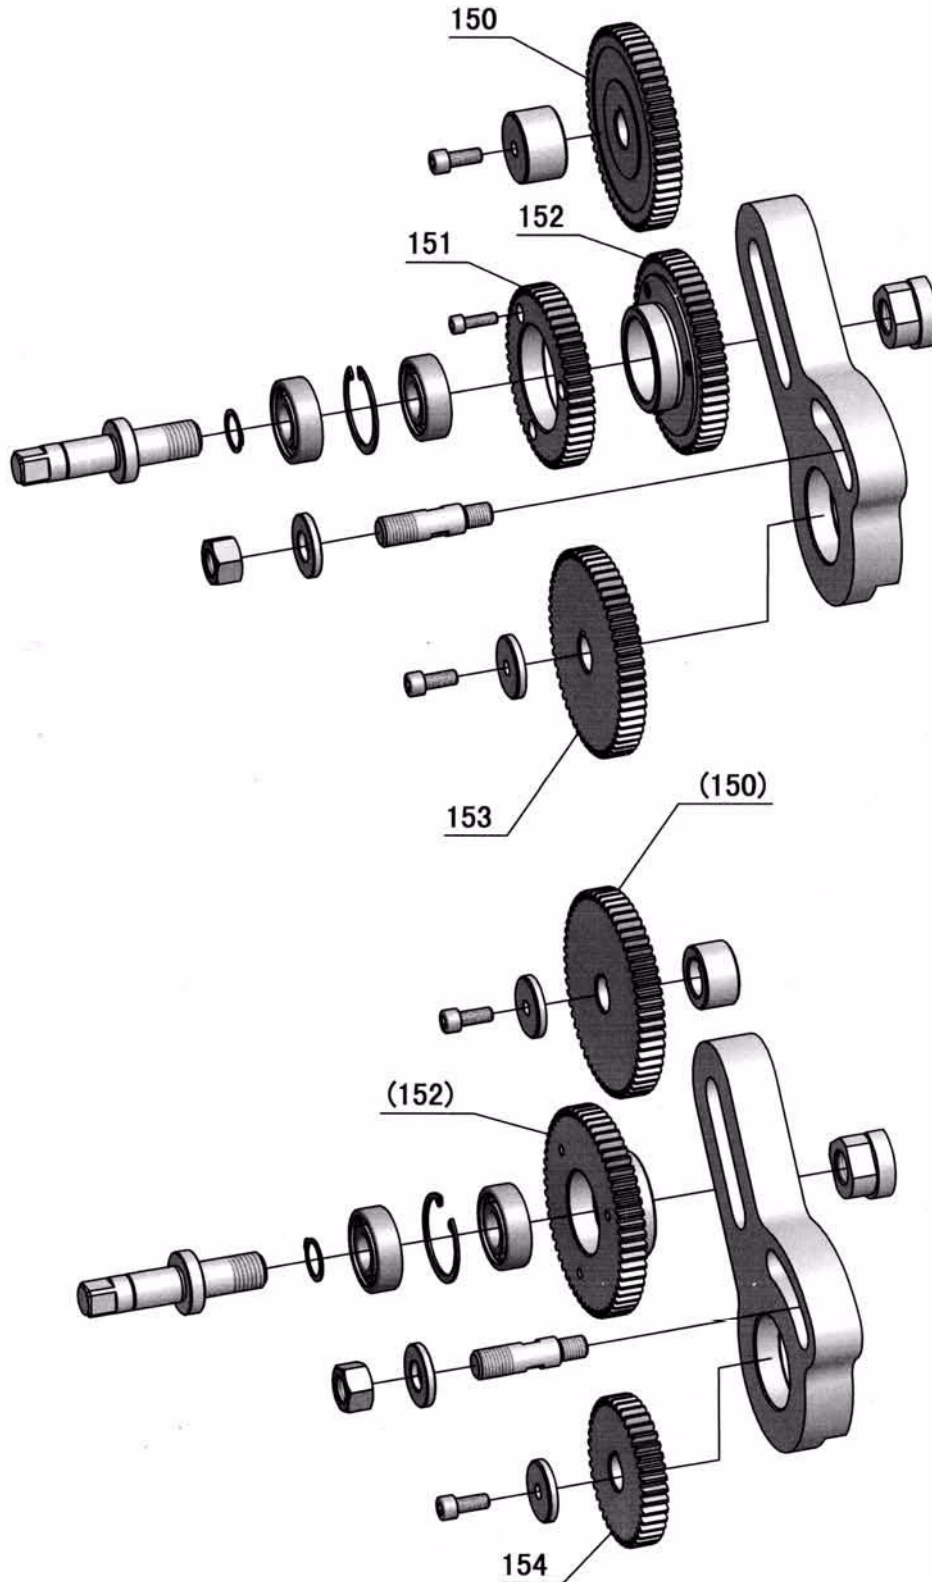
Гитара сменных шестерен (для дюймовой резьбы)
